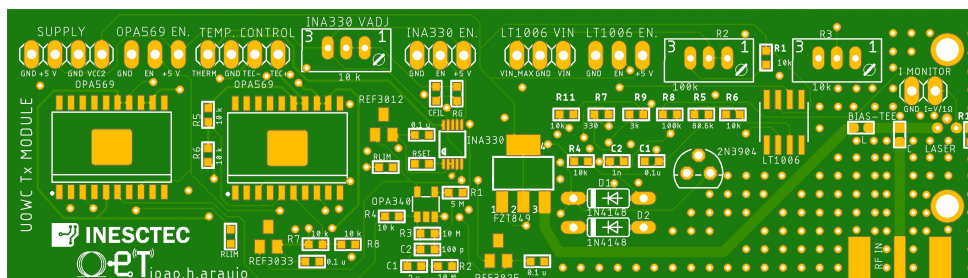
Desenho da PCB protótipo do módulo transmissor.
